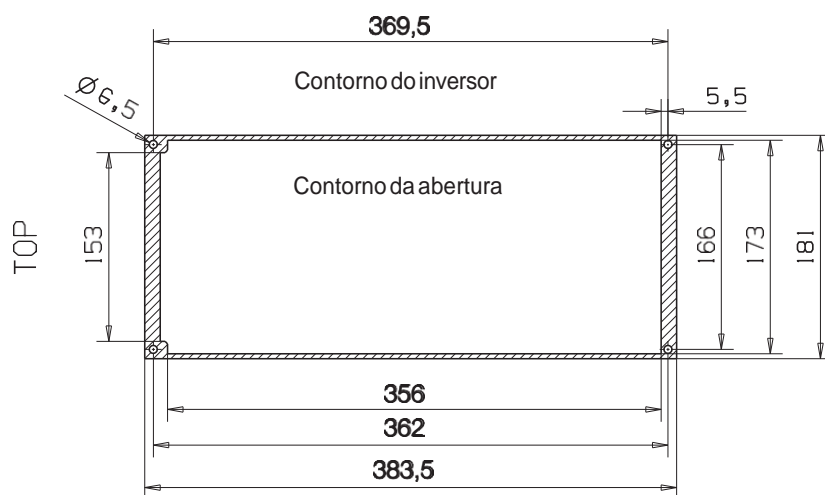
Dimensões do recorte para montagem com flange do MR4 ao MR6 (unidade: mm)
